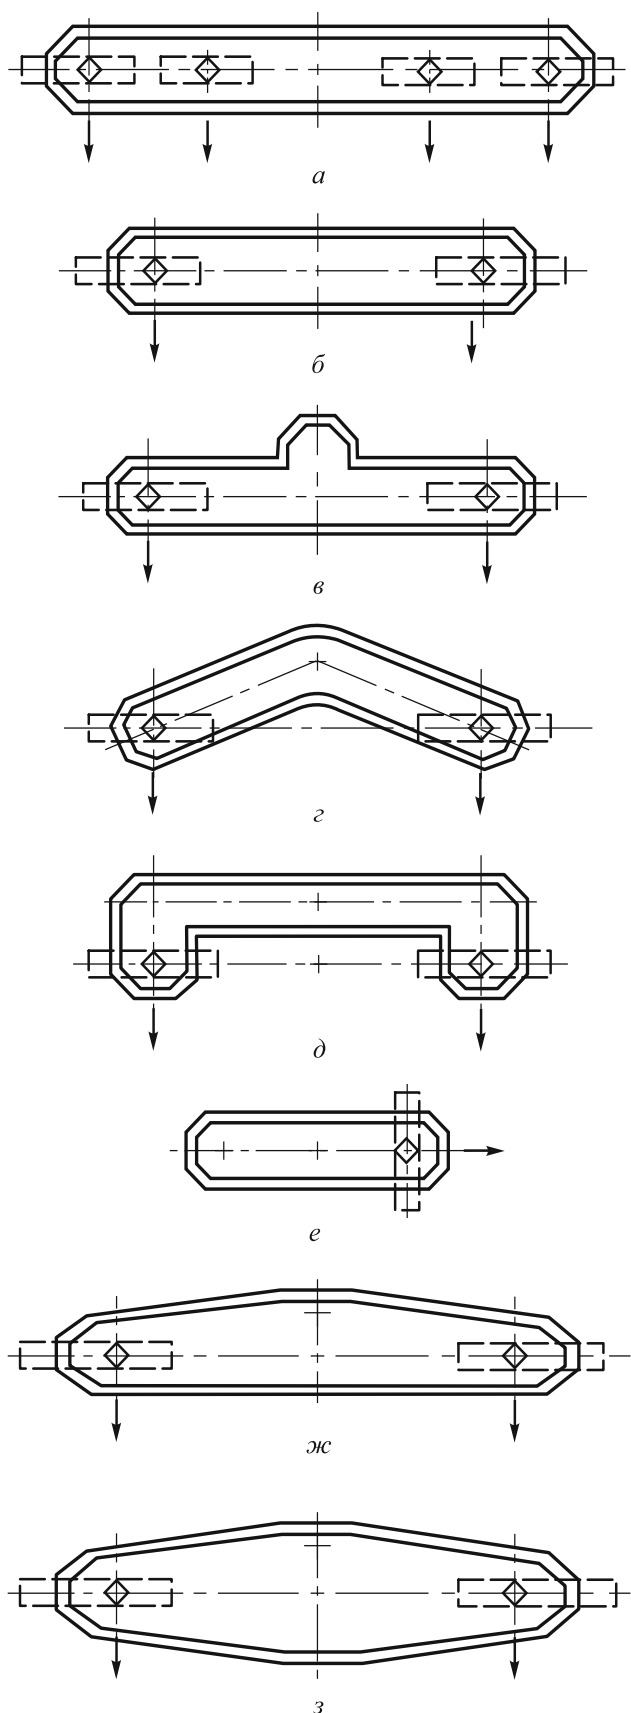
Формы промежуточных двухручьевых ковшей с перегородками, применяемых для разливки слабовых заготовок:
